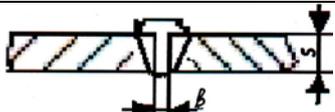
Конструктивные элементы сварного шва С17 по ГОСТ 14771-79
